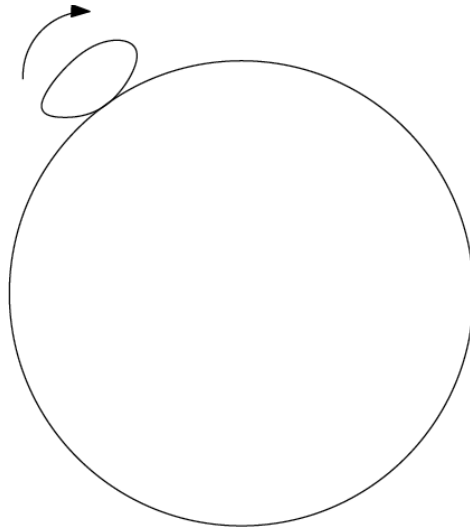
Illustration de la méthode des roulettes, génération du profil conjugué de la roue 1
